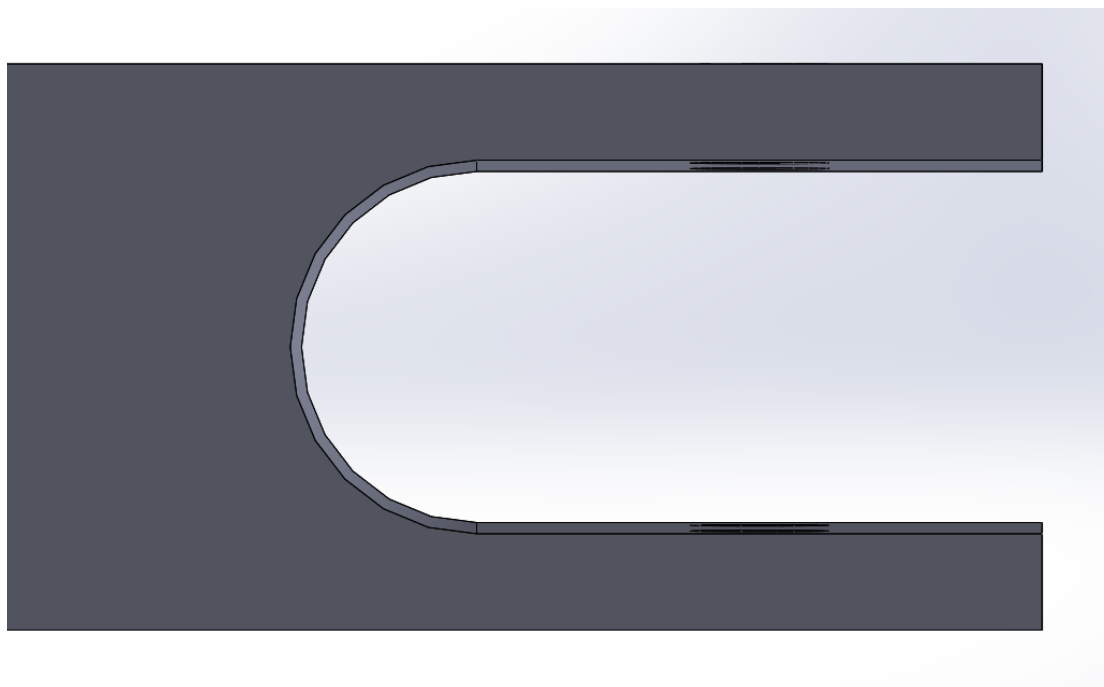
Βάση στήριξης του grinder, σχεδιασμένη στο περιβάλλον του SolidWorks.
